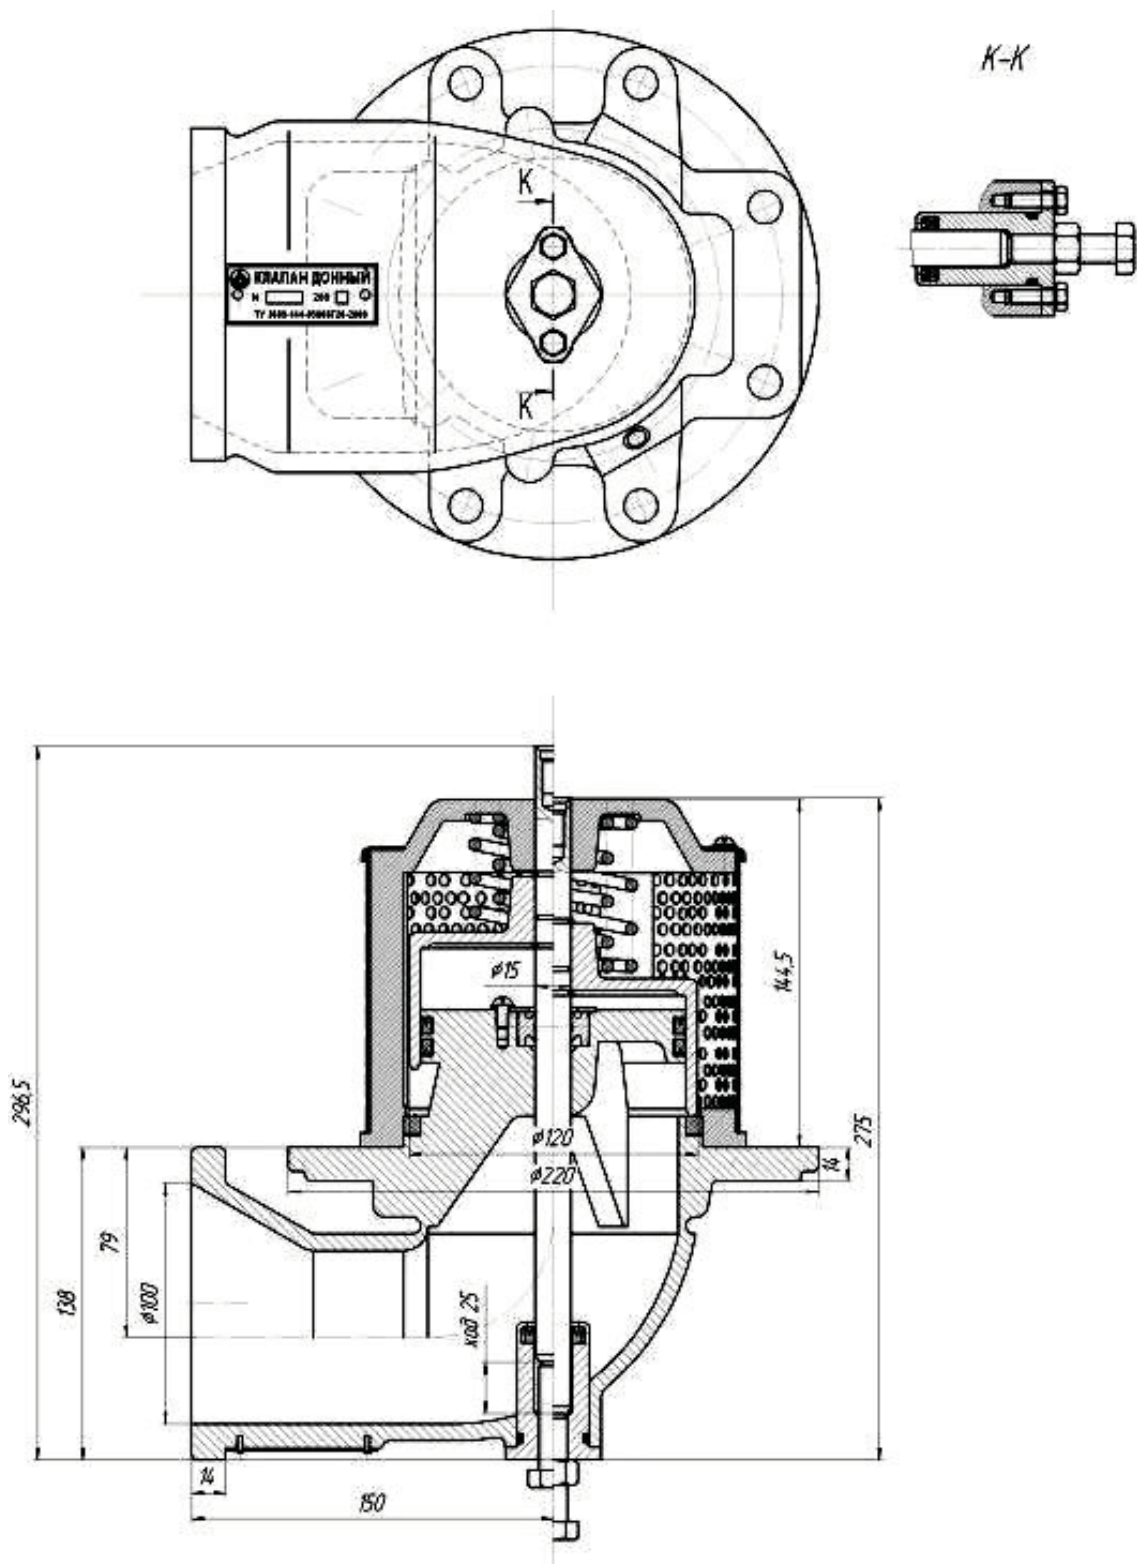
Типовой представитель: клапан донный пневматический низкий профиль с ручным дублированием
